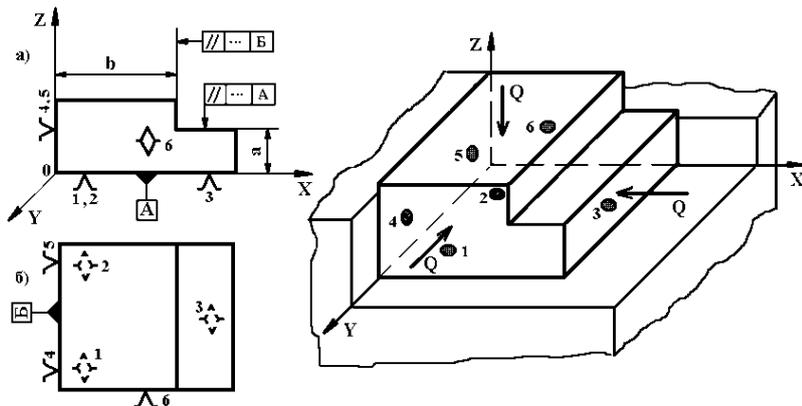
Схема базирования заготовки при фрезеровании.
